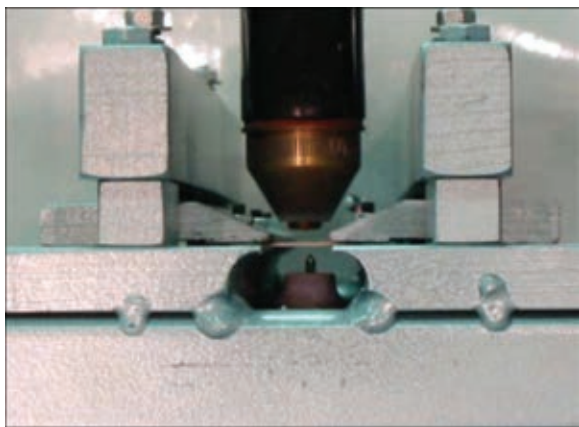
Двухсторонняя плазменно-дуговая сварка и сварка неплавящимся электродом [32]
